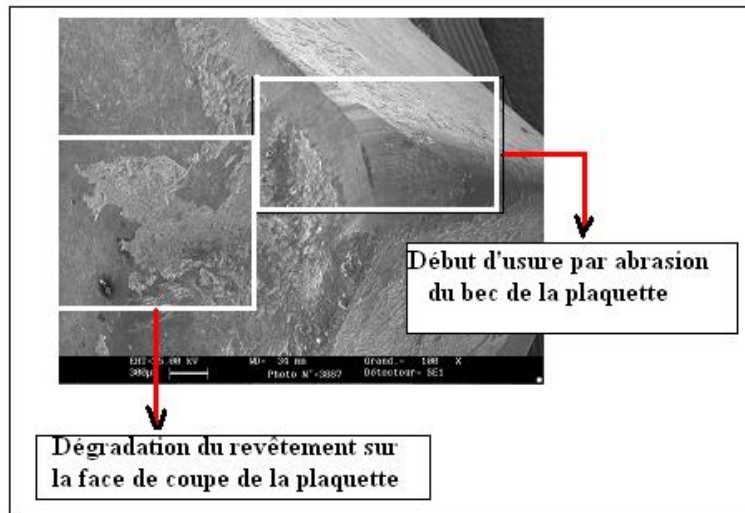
Photo M.E.B : Usure du bec de la plaquette et altération de la couche revêtue sur la face d’attaque
